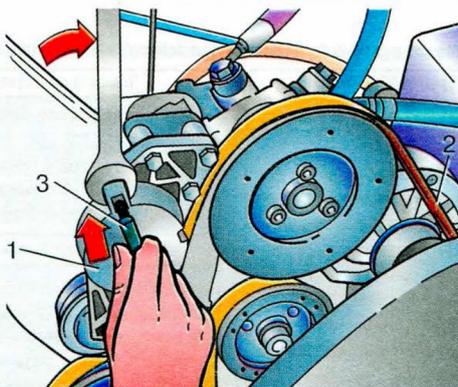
Ослабление натяжения ремня привода агрегатов 5-цилиндрового двигателя: 1 – механизм натяжения ремня привода агрегатов; 2 – ремень привода агрегатов; 3 – штифт фиксирующий
